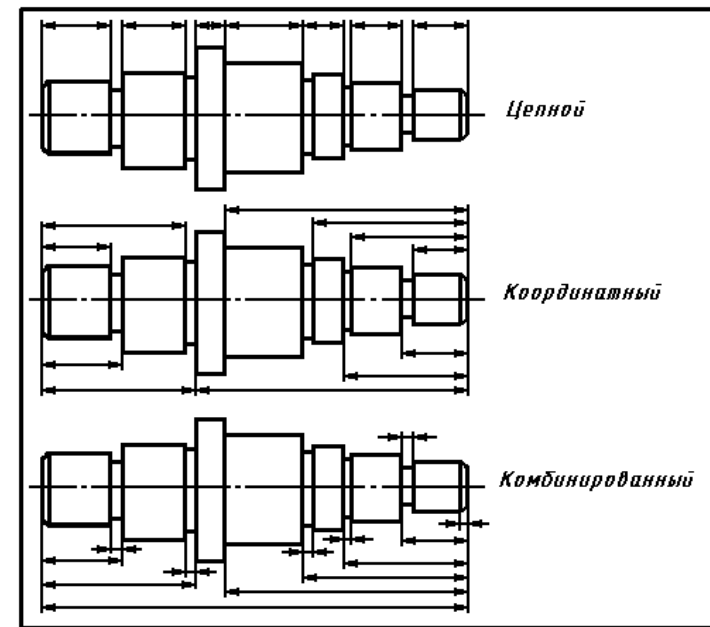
Способы простановки размеров на чертежах типа «вал»
